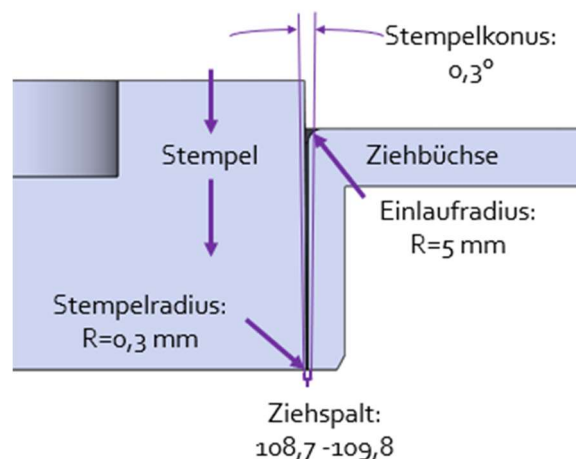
Geometrische Details Tiefziehwerkzeuge
